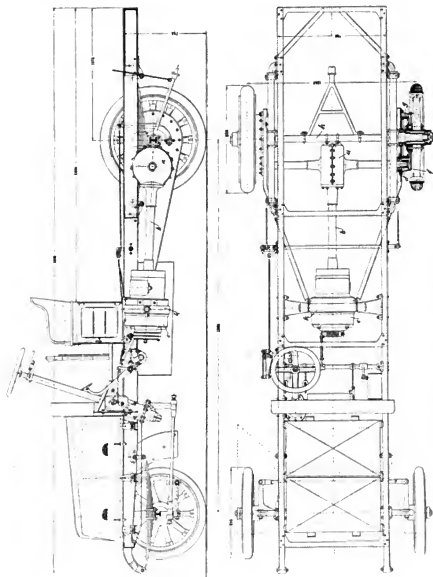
Chassis für schwere Lastwagen der Siemens-Schuckert-Werke.
